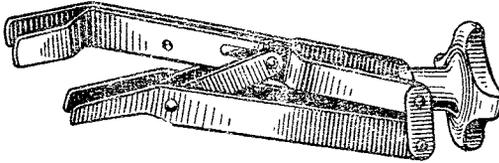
Приспособление для снятия клапанных пружин двигателя
